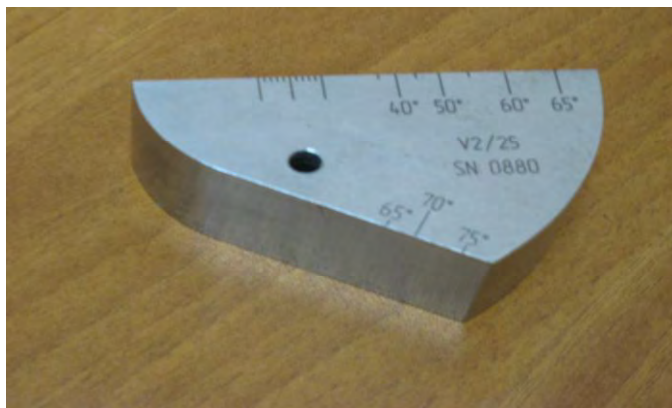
Общий вид калибровочного ультразвукового образца V2/25
